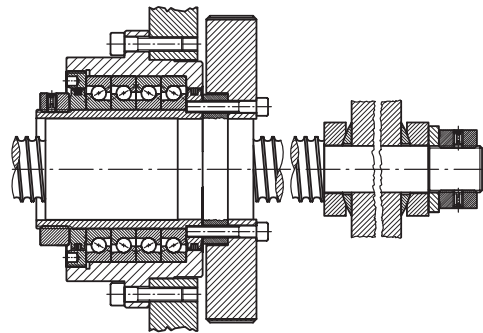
Kugelgewindetrieb mit beidseitig fester Einspannung
